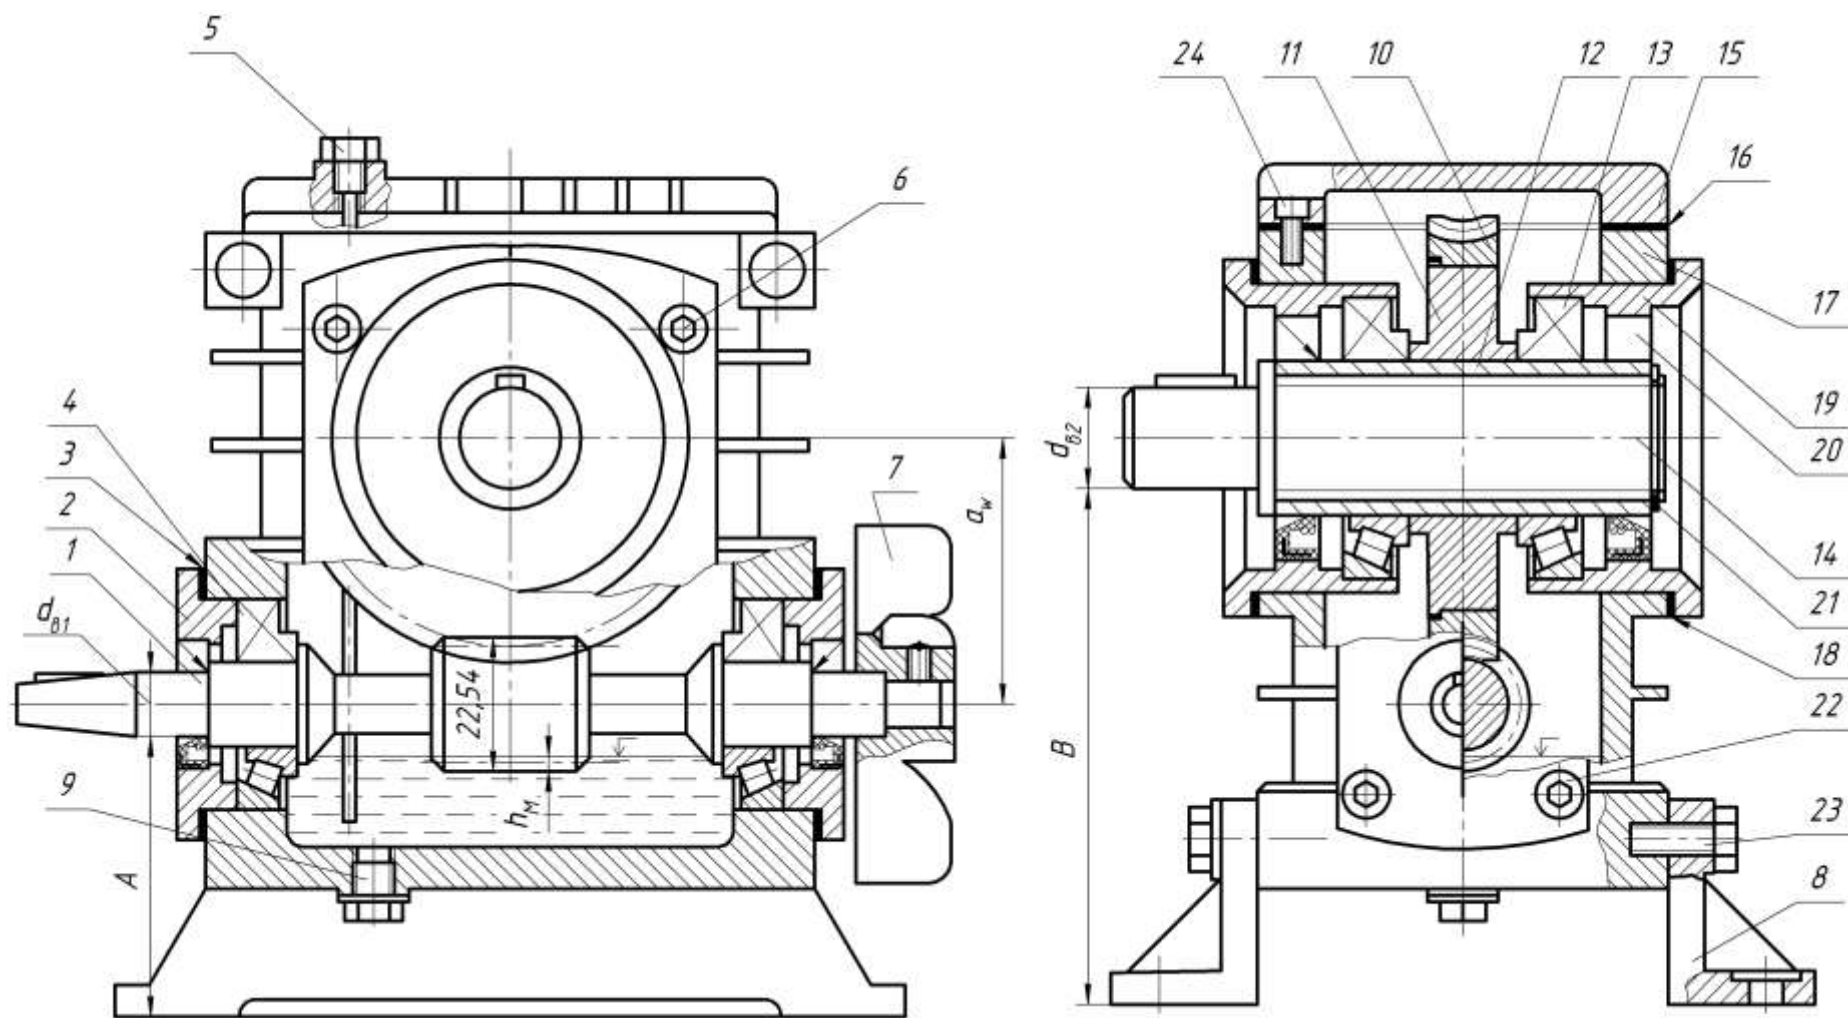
Конструкция червячного редуктора неразъемным корпусом
